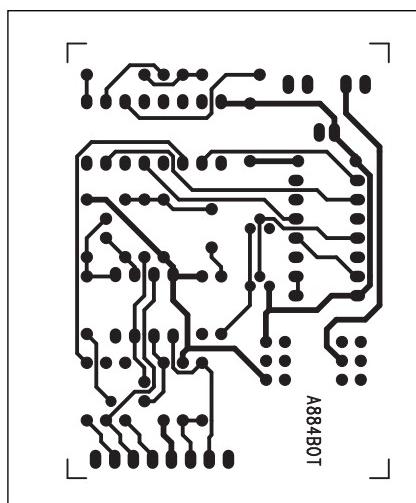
Obrazec desky spojů (strana BOTTOM)
